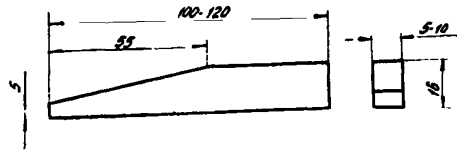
Контрольный штифт для измерения зазора между торцами вала и полумуфты.
